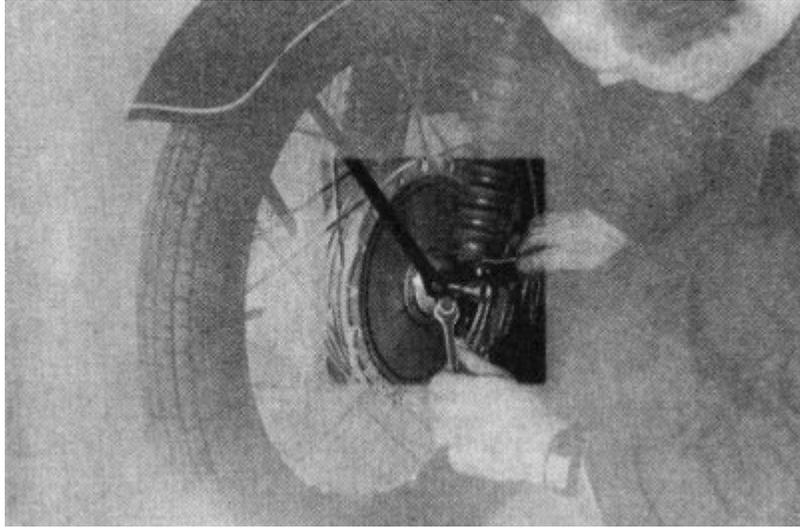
Lockern der Klemmschraube zum Vorderachsausbau
